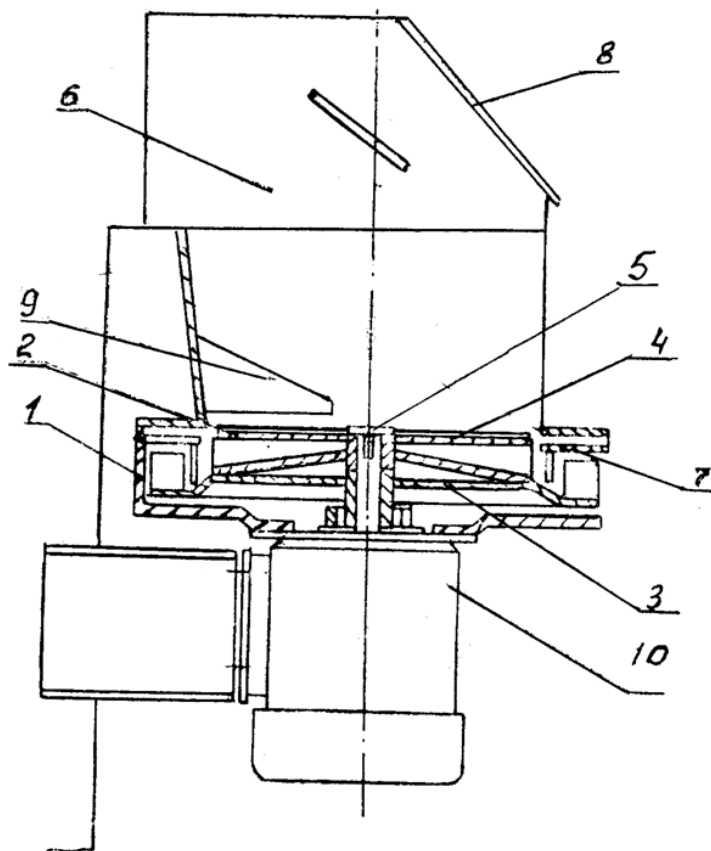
Подрібнювач: 1- корпус; 2- верхній диск; 3- нижній диск із лопатями; 4- ножі; 5- болт; 6- перехідник; 7- дека; 8- кришка; 9- протириз; 10- електродвигун.
